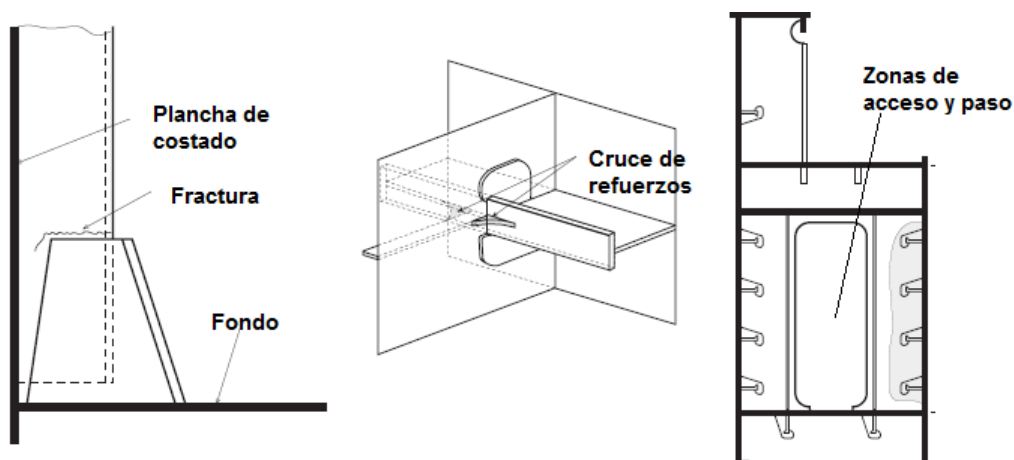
Ejemplos zonas a inspeccionar en la estructura de costado
